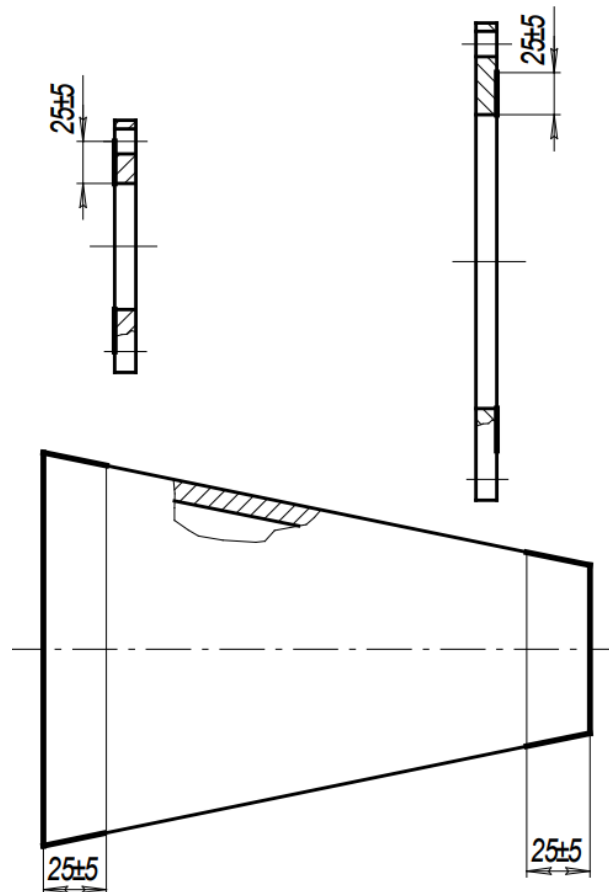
Схема зачистки заготовок під зварювання
